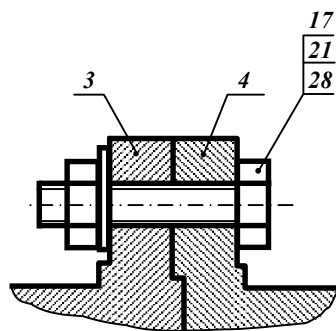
Простановка номеров позиций на сборочном чертеже
